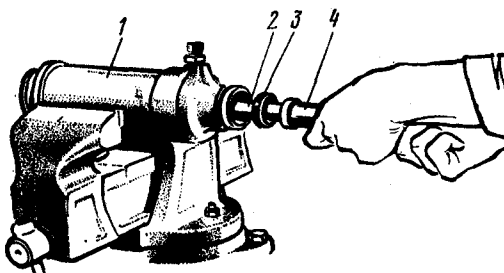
Установка деталей уплотнения штока гидроусилителя:
